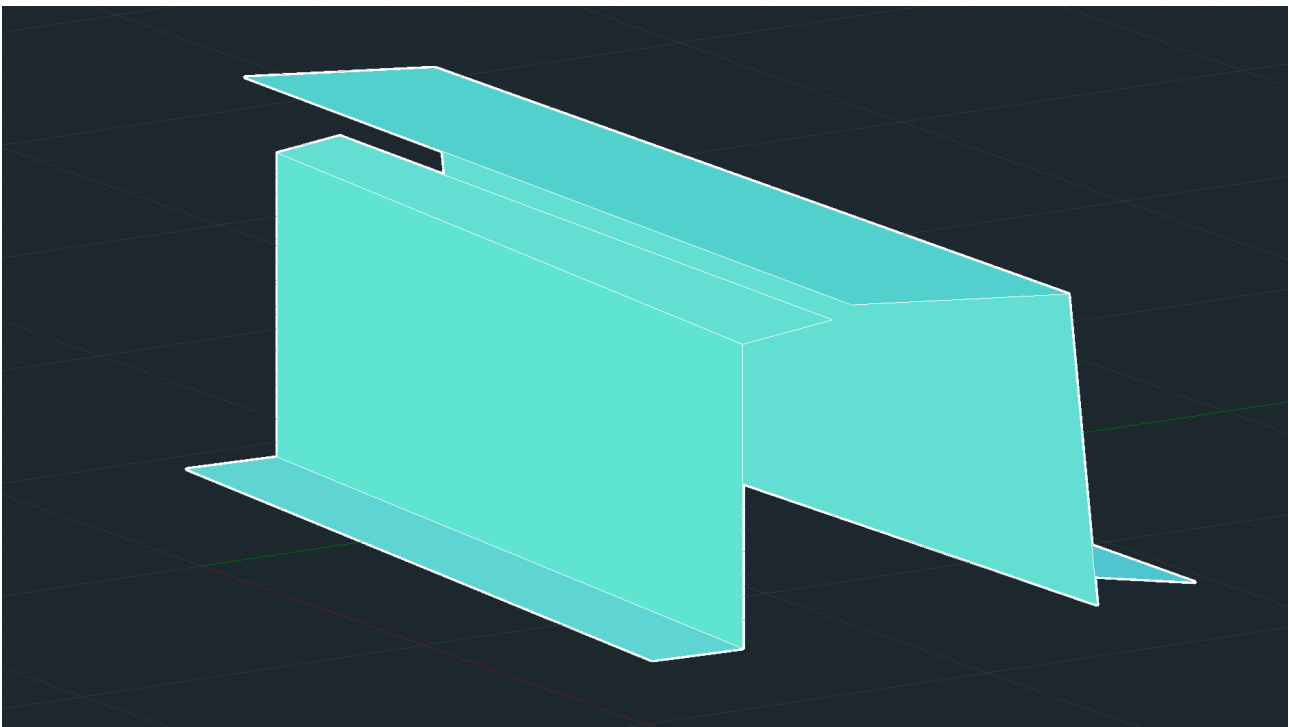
Modelo completo en Cad (Vista Norte))
